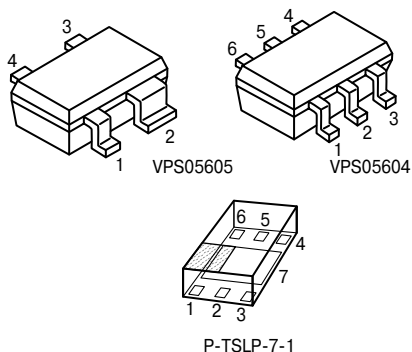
Корпуса типа SOT и TSLP для MMIC (4...7 выводов).
